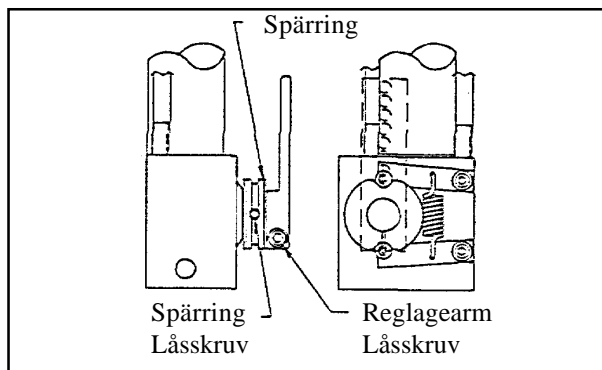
Korrekt installation av växelgivare till backslagsarm.
